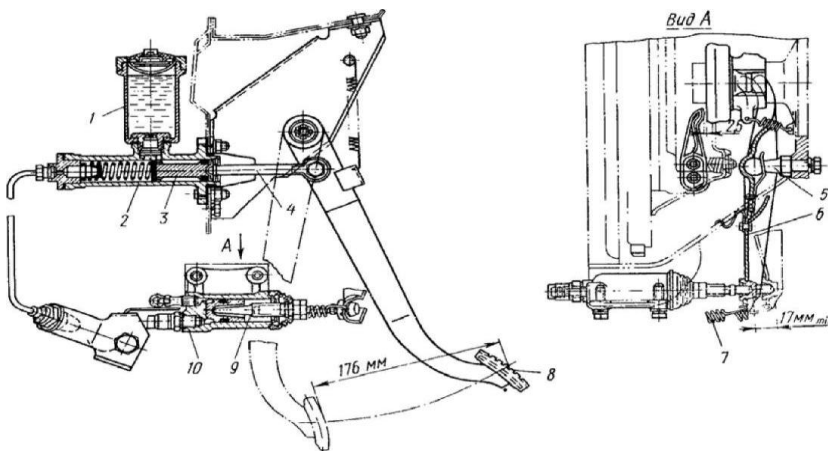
Гідравлічний привід зчеплення: 1 - бачок; 2 - головний циліндр; 3 - плунжер; 4 - штовхач; 5 - опора вилки; 6 - вилка; 7 - пружина; 8 - педаль зчеплення; 9 - штовхач робочого циліндра; 10 - робочий циліндр.
